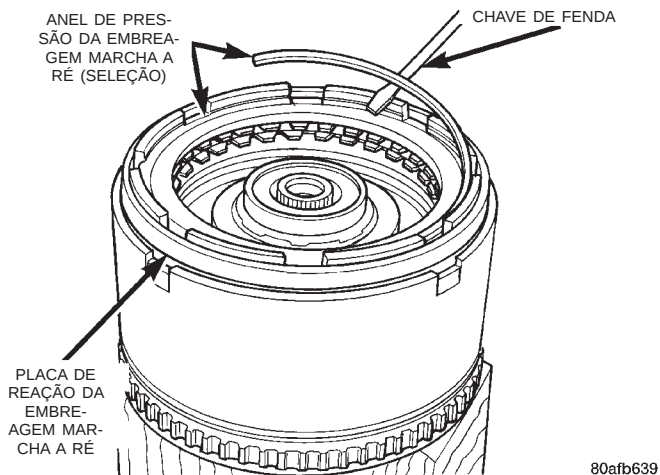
Instalação do Anel de Pressão da Embreagem Marcha a Ré
